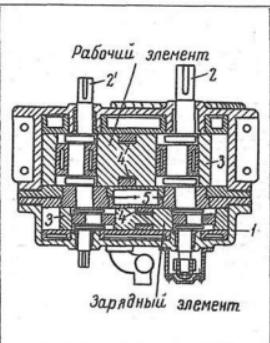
Конструкция основных элементов ротативно-поршневого двигателя «Рогус»
